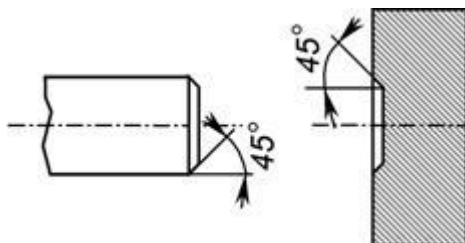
Разделка поверхностей деталей под ротационную сварку.
